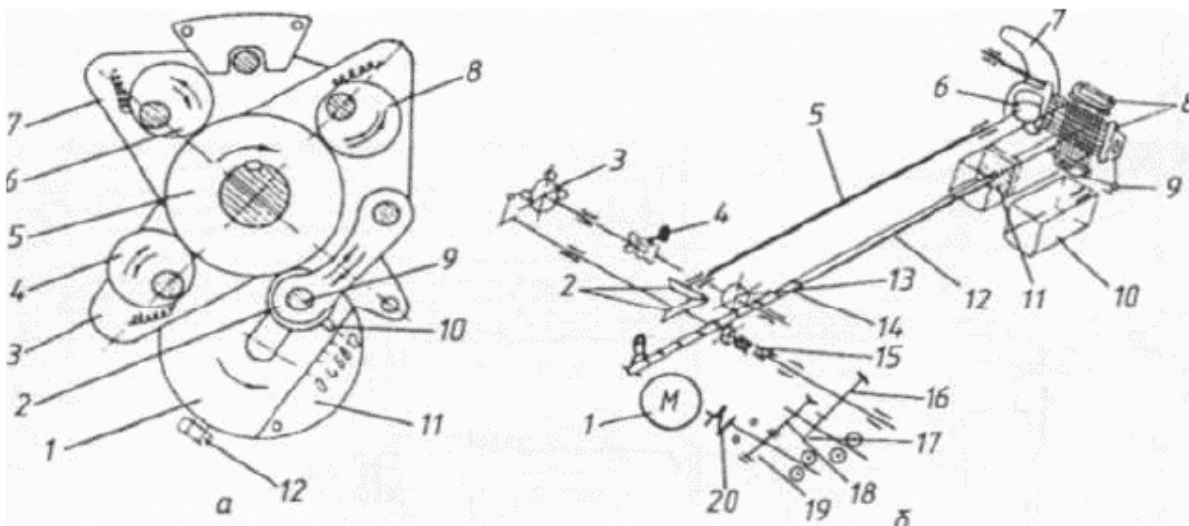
Механизм циклической подачи и кинематическая схема шпигорезки ФШМ-2:
